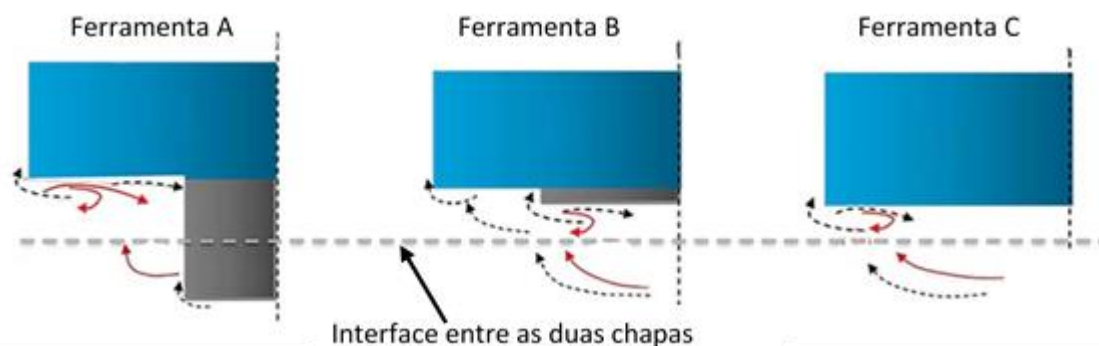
Representação do fluxo de material em soldadura por FSSW utilizando diferentes geometrias do pino (adaptado de Leon e Shin, 2016)
